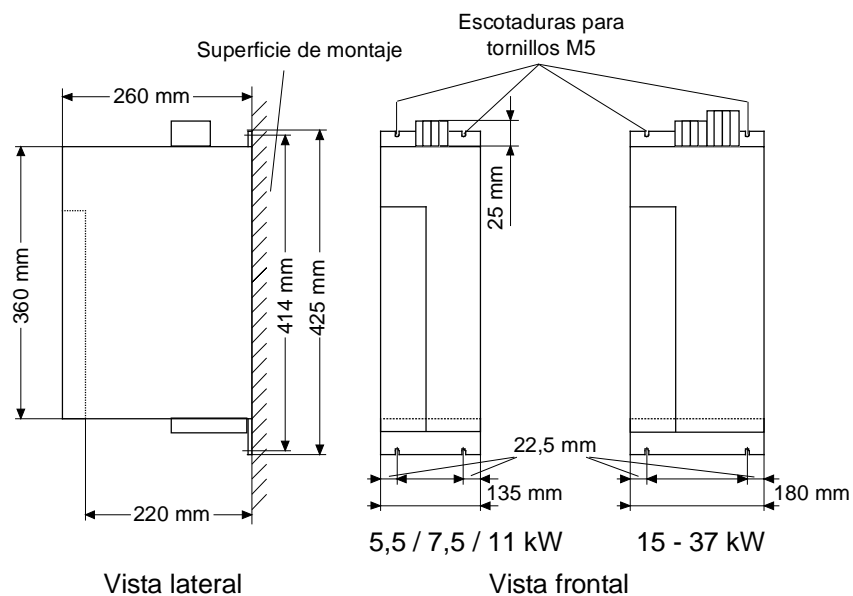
Croquis acotados para equipos con anchuras de 135 mm y 180 mm
